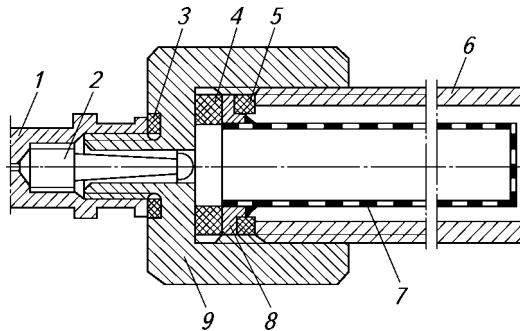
Схема форсунки типа 1Б-06 для распыления воды:
